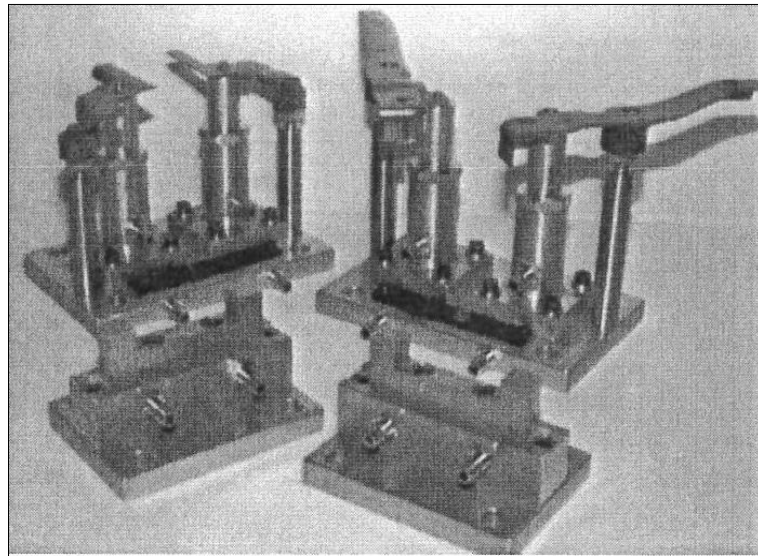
Ejemplo de un dispositivo de sujeción para ser usado en soldadura por proyección.
